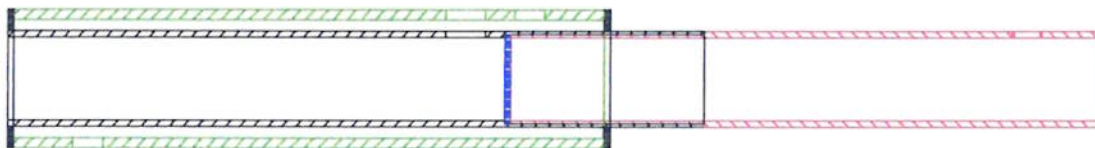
Desenho de conjunto da câmara montada.
